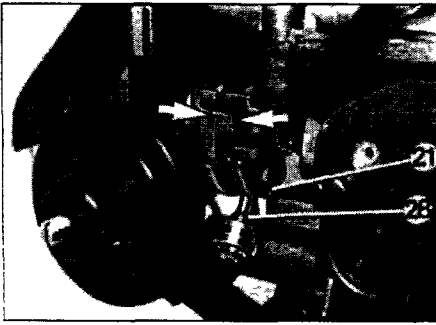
Регулировка пусковых оборотов - карбюратор снят
